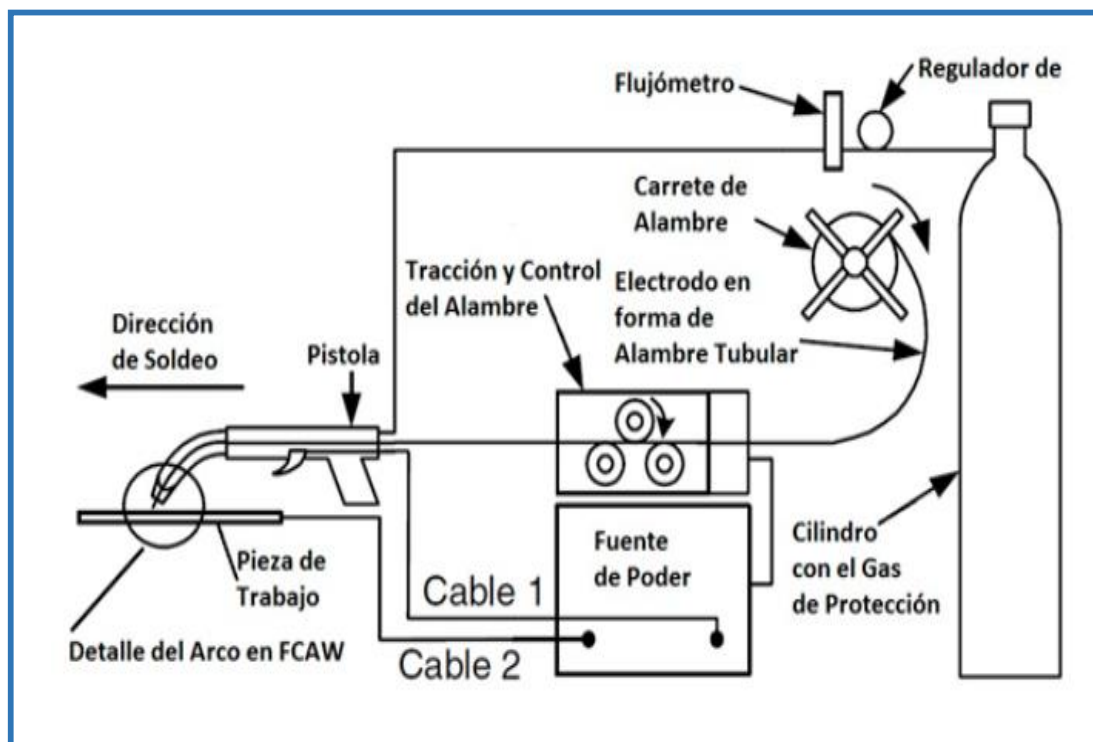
Esquema de equipo de soldadura FCAW
